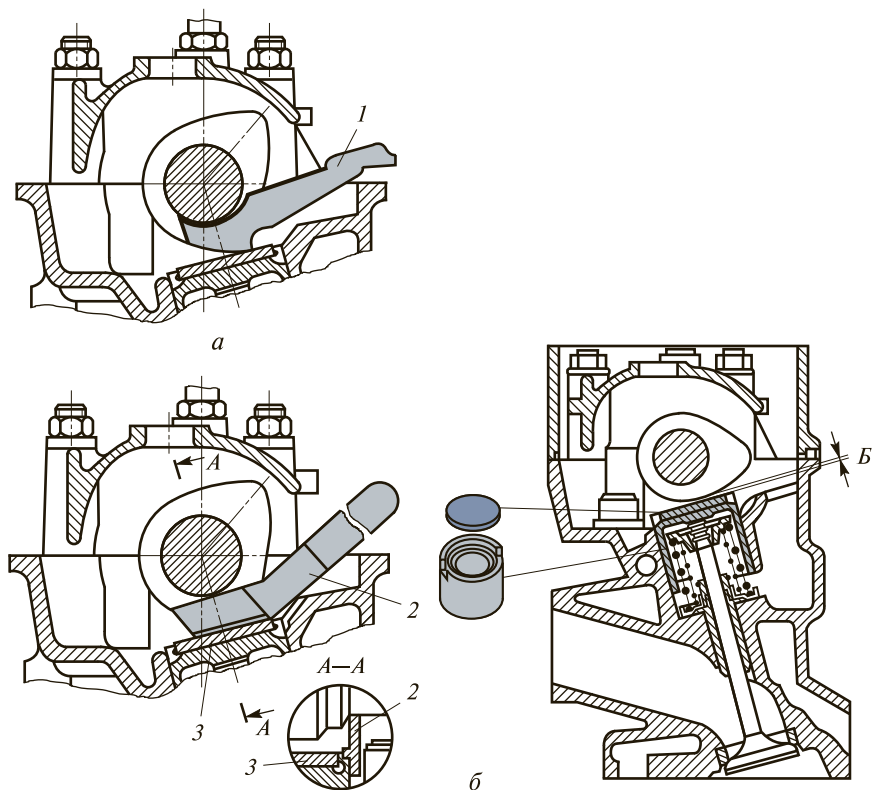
Регулировка зазора в распределительном механизме двигателя ВАЗ-2108, -2109:
